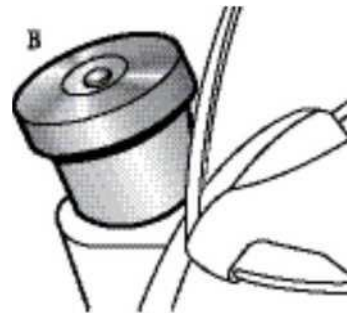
10 Tapa de boquilla de carga de aceite de cámara de engranaje de temporización de motor diesel
